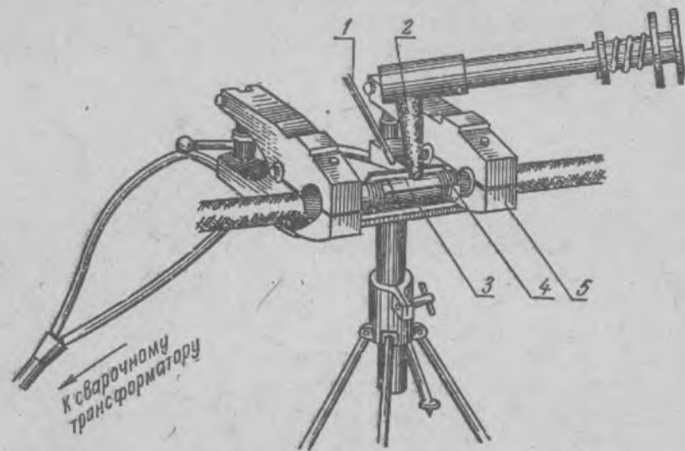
Соединение жил сваркой в открытой форме
